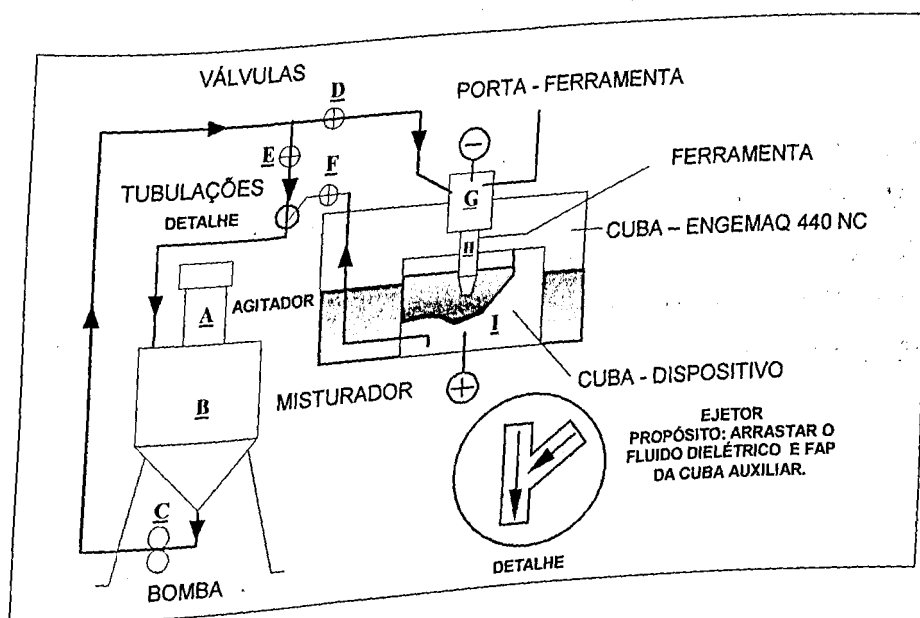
Dispositivo auxiliar de mistura e injeção do FAP.
